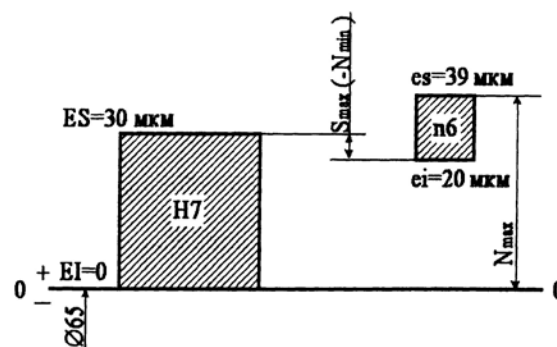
Схема розташування полів допусків посадки 65 H7/h6
